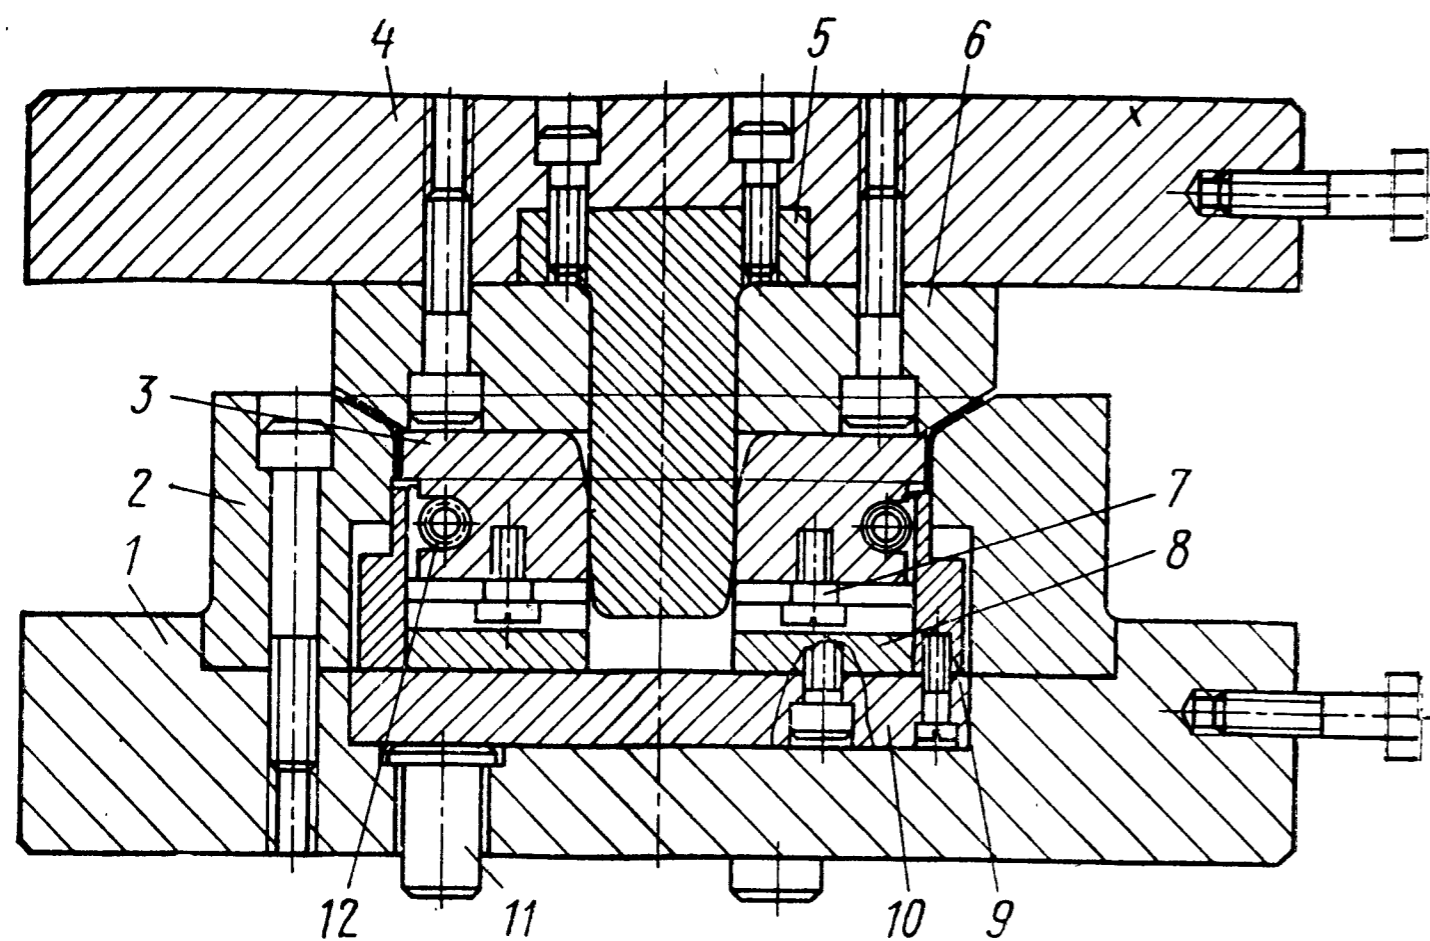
Штамп для предварительной растяжки и отбортовки ступенчатого кольца
